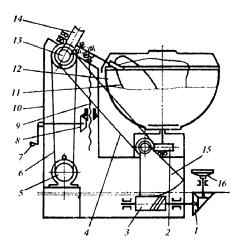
Кинематическая схема смесителя молели МЛ-100:
